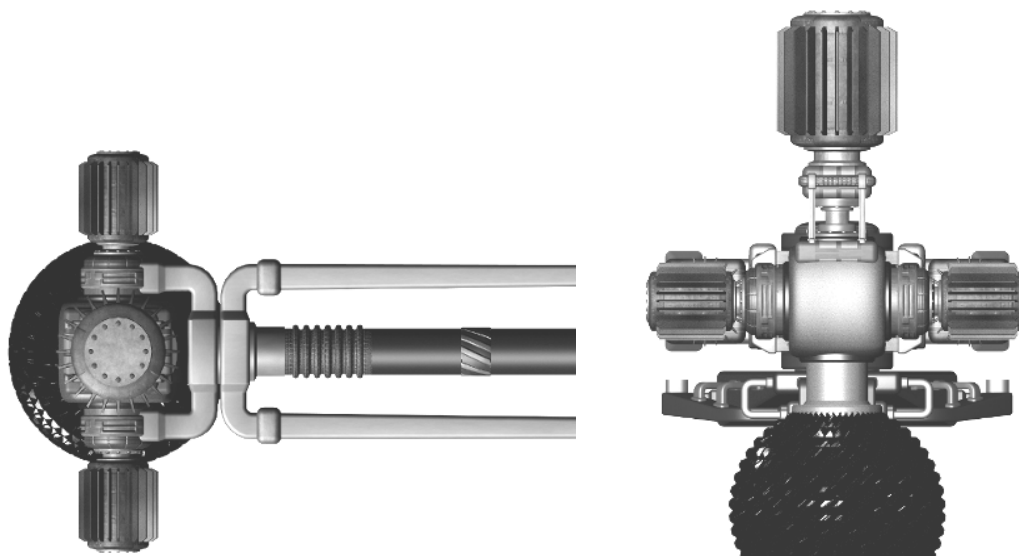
Внешний вид рабочего узла фрезы. Вид сверху (слева) и вид спереди (справа)
